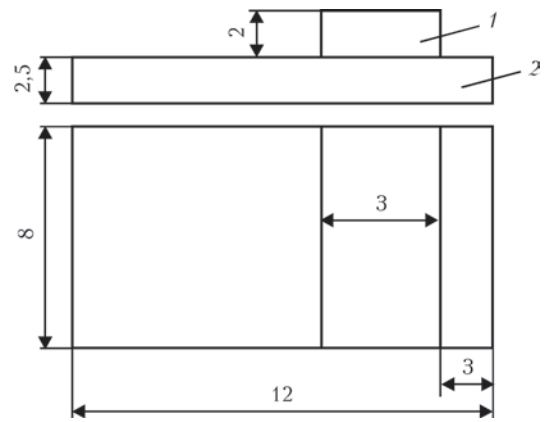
Схема образца для испытаний на срез: 1 — участок медной пластины; 2 — стальная пластина
